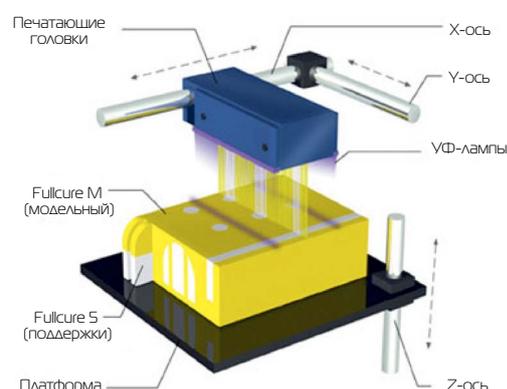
Схема фотополимерного принтера на основе струйной печати
